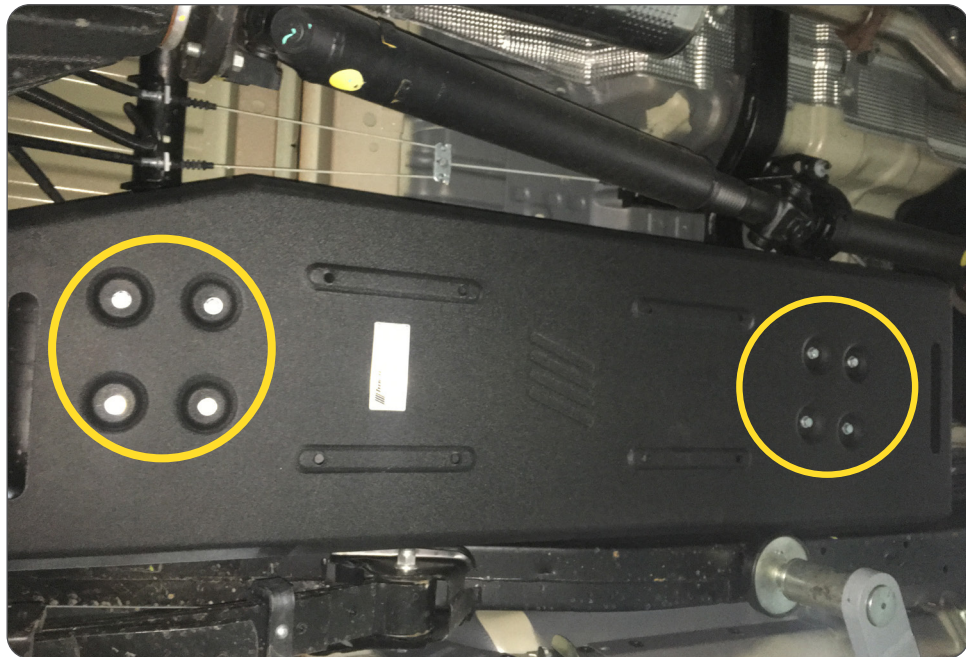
montierter Unterfahrerschutz/ mounted skid plate
